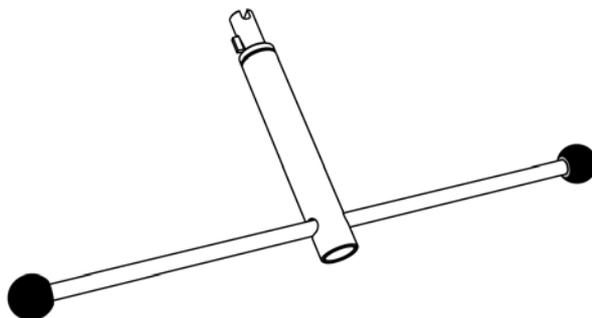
Стандарт: Однорычажное управление с черной рукояткой и кодировкой универсального рычага. Альтернатива 1: Приводной рычаг с красной рукояткой для заземления и снятия заземления и приводной рычаг с черной ручкой для выключателя нагрузки. Альтернатива 2: Однорычажный привод с помощью матового рычага и без кодировки.
